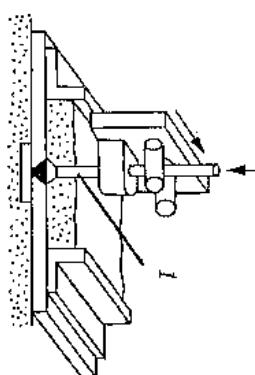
Автоматическая дуговая сварка под слоем флюса
